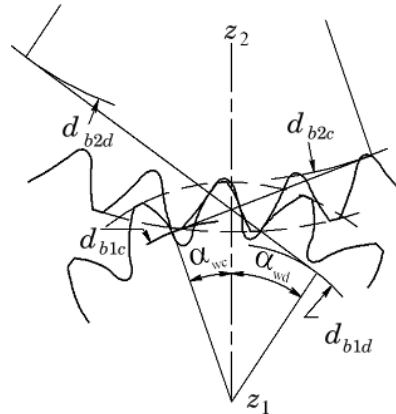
Схема зацепления зубьев шестерни и колеса с асимметричными зубьями [13]
